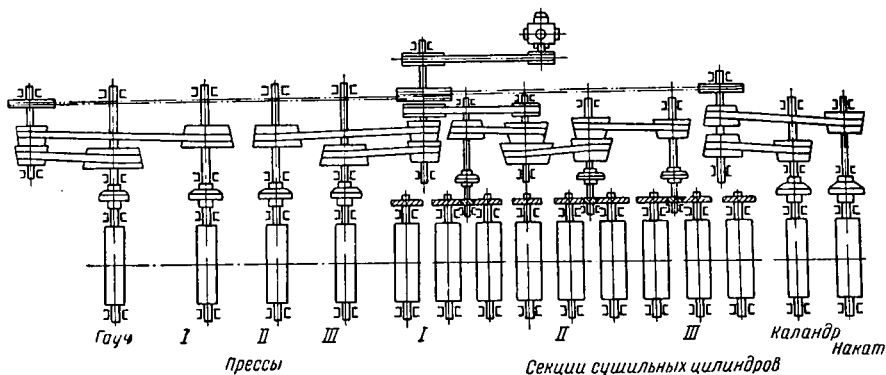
Схема привода бумагоделательной машины с параллельными валами
